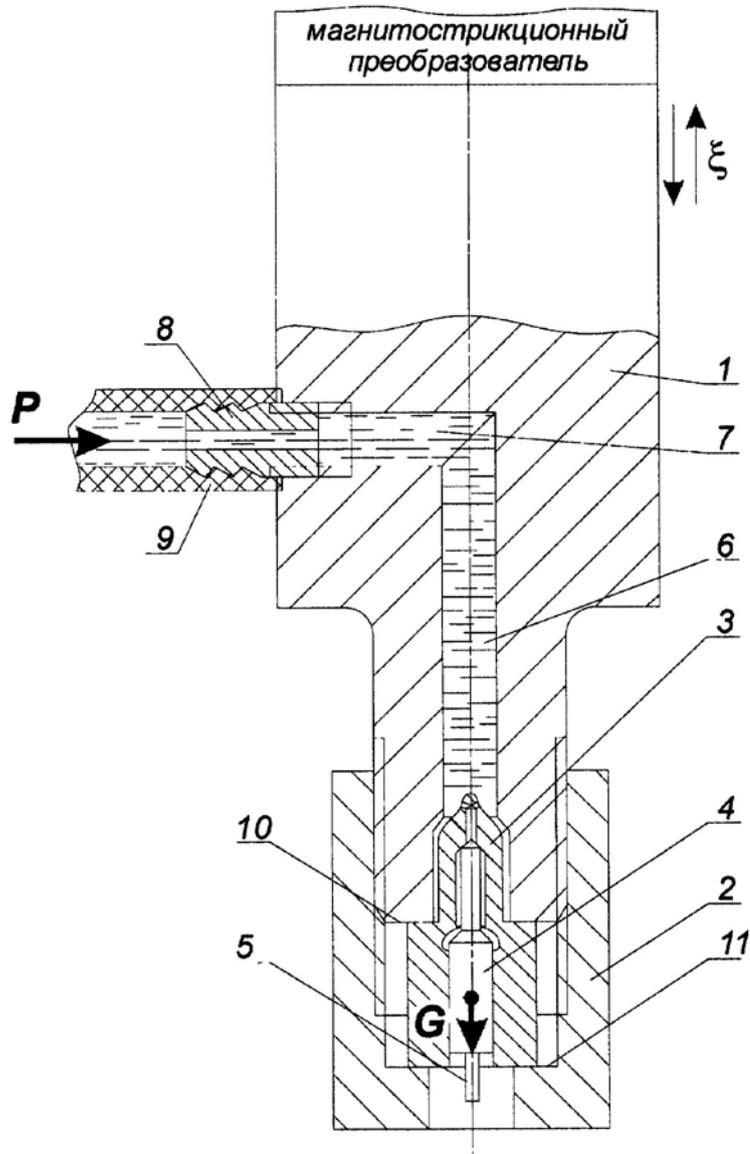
Патент RU 103774 U1. Ультразвуковое устройство для разборки распылителя форсунки: 1- стержневой концентратор; 2- упор; 3- распылитель; 4- запорная игла; 5- хвостовик; 6- осевое отверстие; 7- канал; 8- штуцер; 9- шланг; 10- торец концентратора; 11- опорная поверхность.
